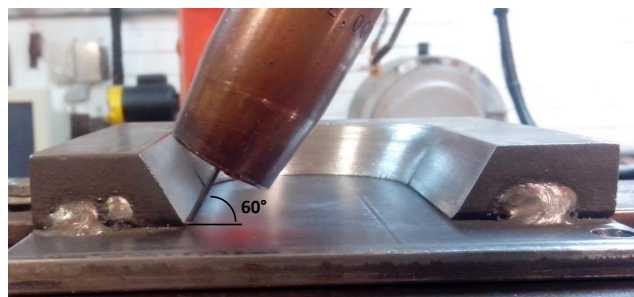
Posição da tocha de soldagem a 60° com respeito à placa mata-junta
